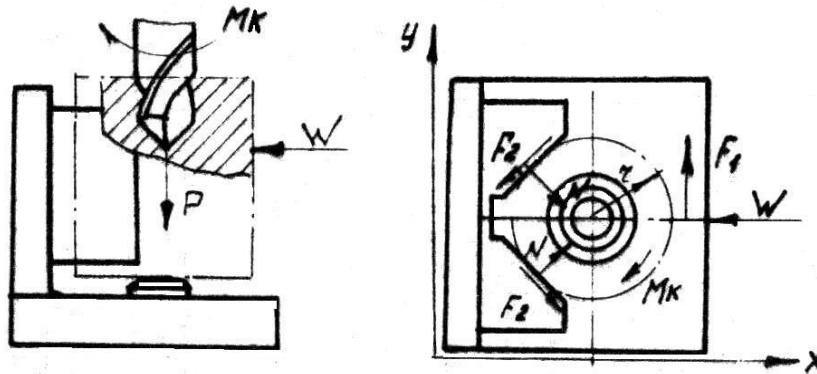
Схема розрахунку затискних зусиль при обробці заготовки на свердлильному верстаті установленій в призмi з прихватом
